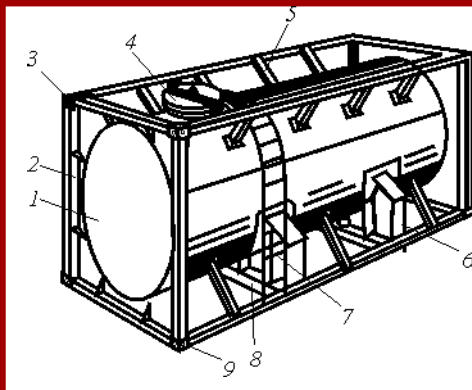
Специализированный контейнер-цистерна СК-3-5 для наливных грузов: 1 — котел; 2 — каркас; 3 — верхние фитинги; 4 — люк с крышкой; 5 — раскосы; 6 — жесткие опоры; 7 — лестница; 8 — поперечные балки; 9 — нижние фитинги
